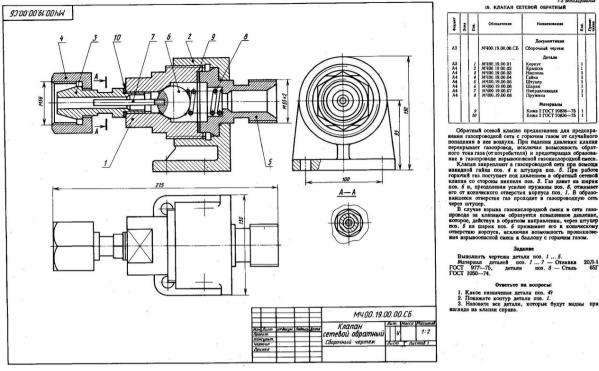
Вариант сборочного чертежа для моделирования.
